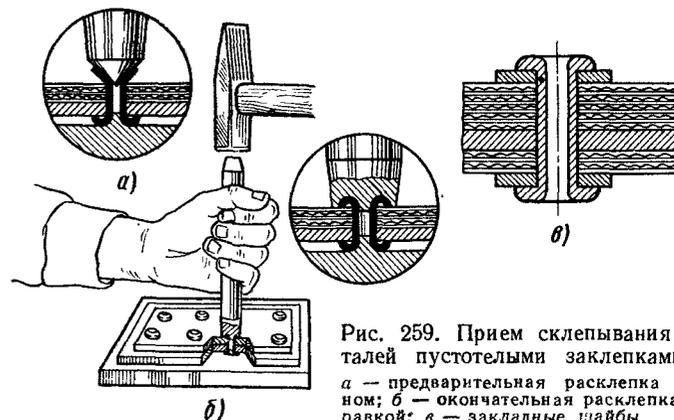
Прием склепывания деталей пустотелыми заклепками:
